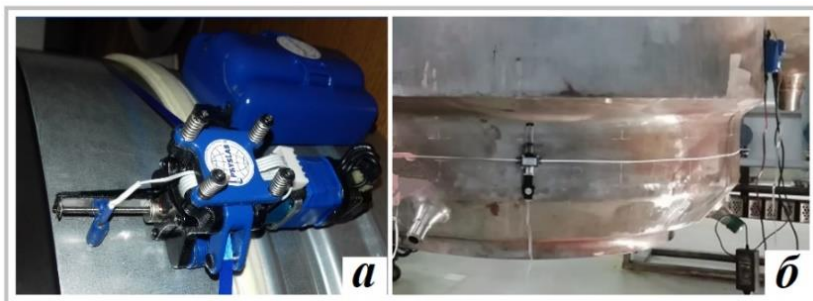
Автоматизированный прибор ЭНК сварных соединений (а).
